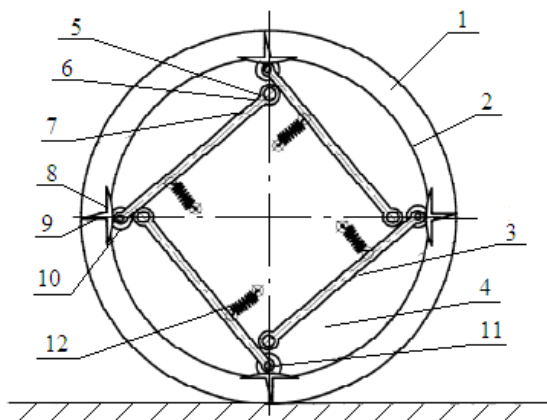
Колісний рушій в неактивному стані (вид збоку):
